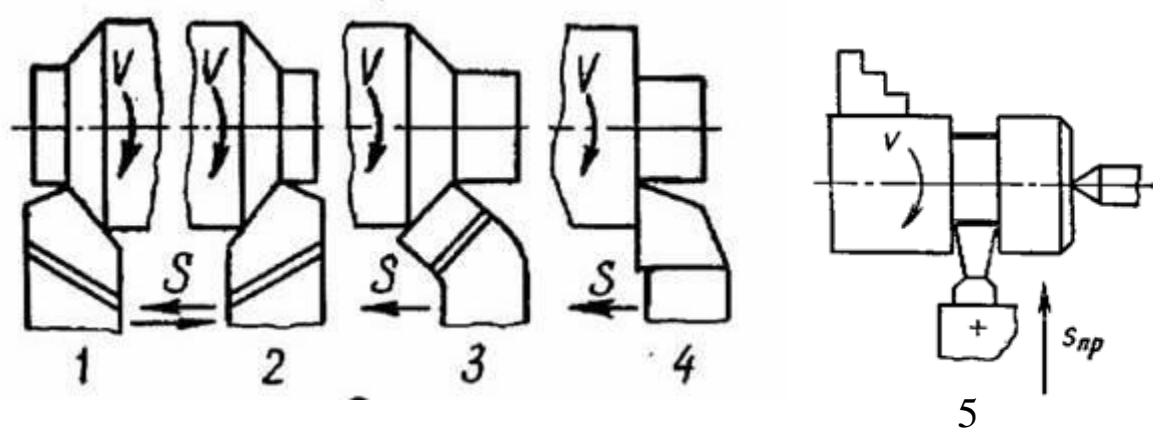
Эскизы обработки наружных цилиндрических поверхностей:
